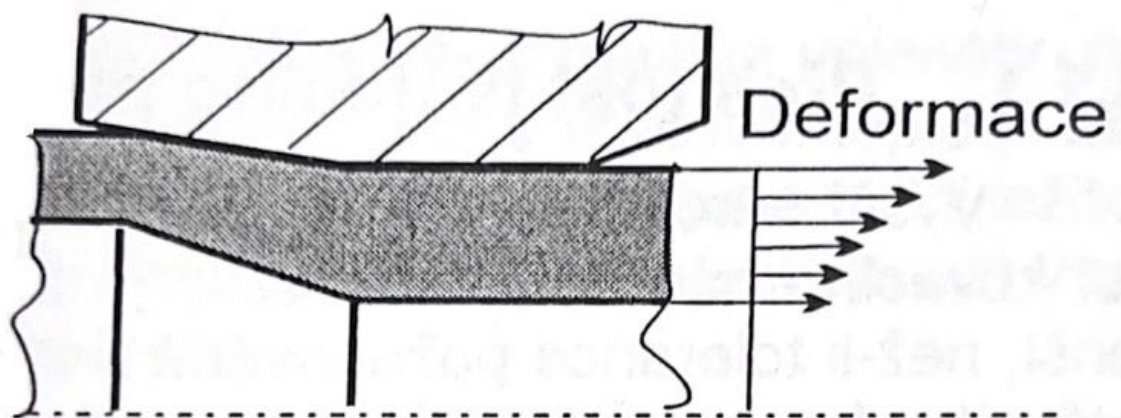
Princip radiálního kování drážkovaného vývrtnu hlavně – podle [25].
